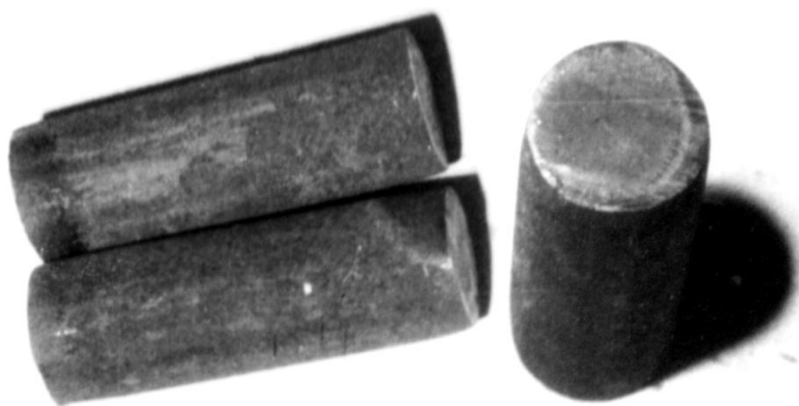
Образцы из стали 38X2МЮА, отрезанные в штампе новой конструкции
